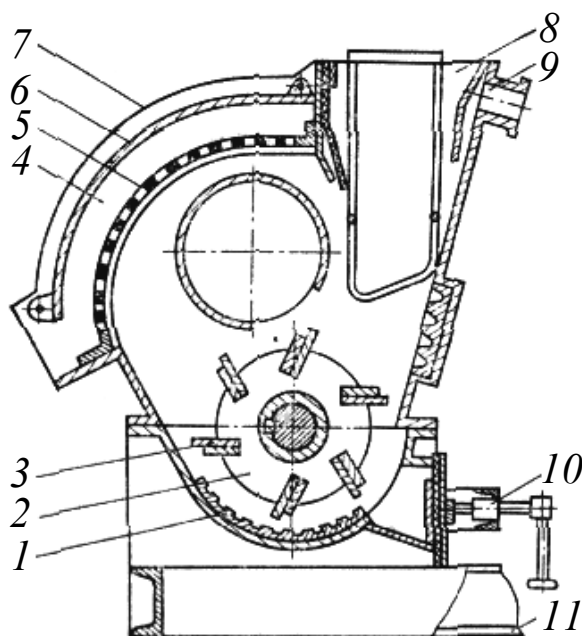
Фрезерно-струйная мельница типа ФСМ: 1 – диспергирующая рифленая плита; 2 – лопастной ротор; 3 – лопасть; 4 – лоток; 5 – выходная решетка; 6 – отражательный щиток; 7 – борт; 8 – приемный бункер; 9 – патрубок для подачи воды; 10 – механизм открывания и закрывания крышки ловушки; 11 – рама
